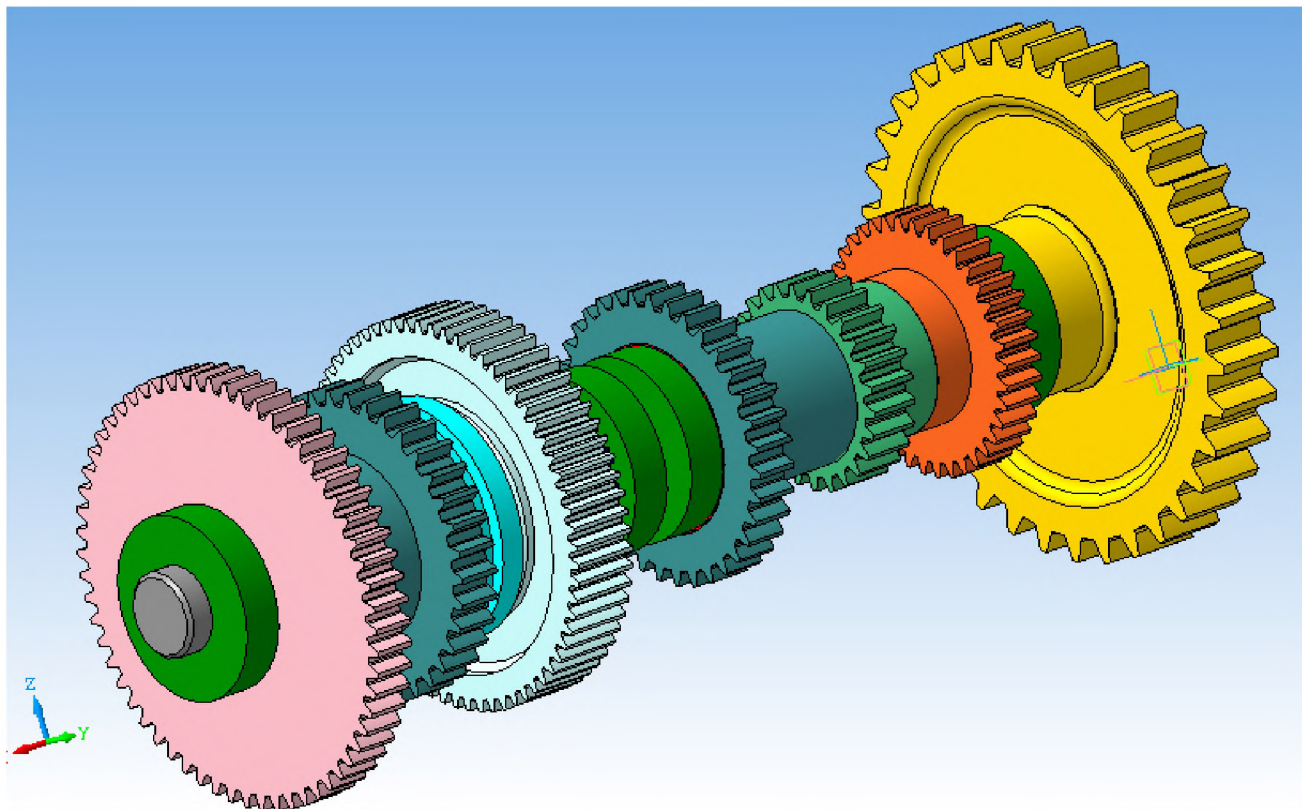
3D модель складання валу коробки подач горизонтально-фрезерного верстата мод. 676
